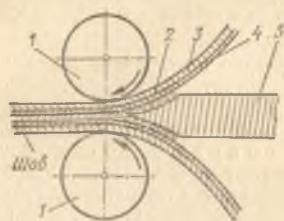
Схема термоконтактной сварки на машине фирмы «Пфафф»
